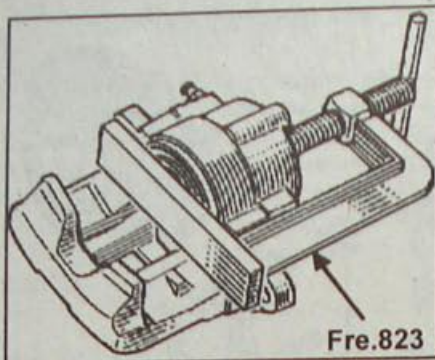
Использование приспособления Fre. 823 для вдавливания поршня в суппорт
